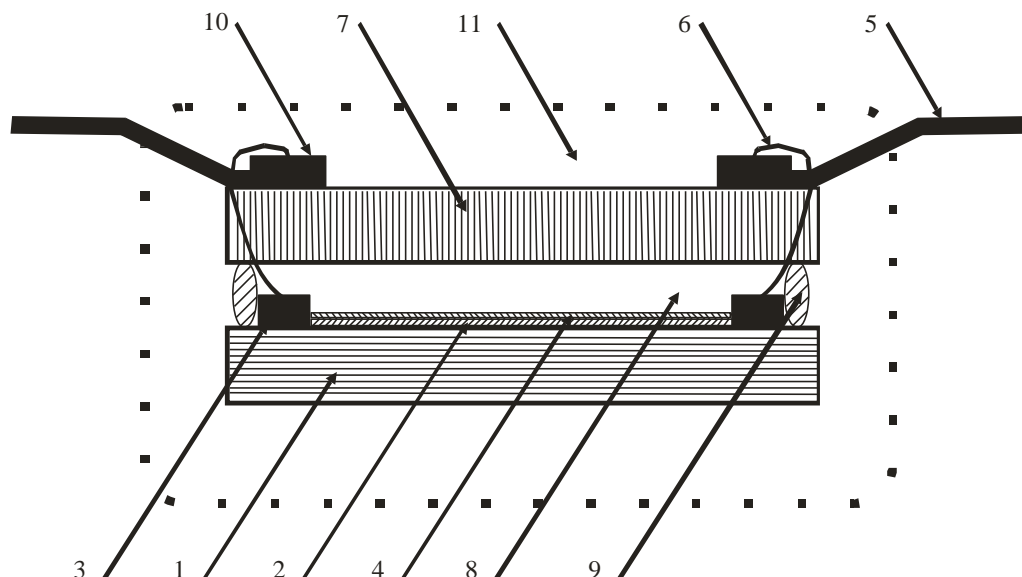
Схематический разрез корпуса резистора-предохранителя: 1 – кристалл резистора-предохранителя; 2 - пленка титана; 3 - контактные площадки; 4 - пассивирующее покрытие из диоксида титана; 5 - внешние контактные ножки корпуса; 6 - золотая проволока диаметром 30 мкм; 7 – крышка; 8 – воздушный зазор; 9 – акриловый герметик; 10 – эпоксидная смола; 11 – высоковольтный компаунд.
